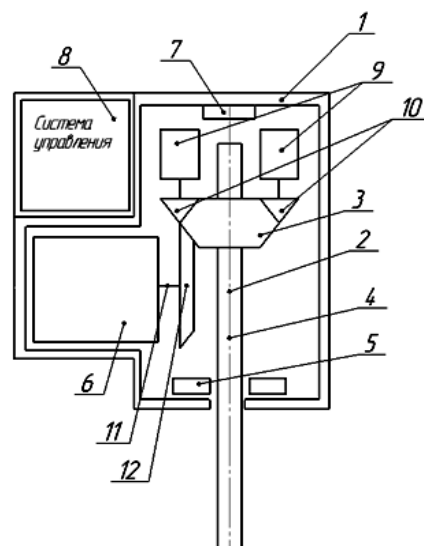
Конструктивная схема электромеханического привода штанги стыковочного устройства
